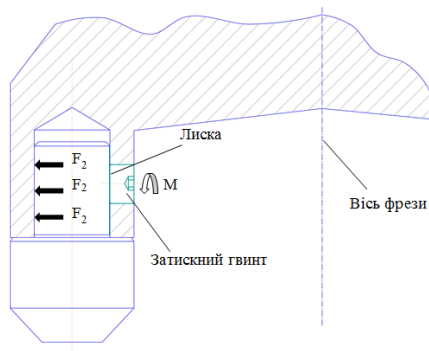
Касета з лискою на хвостовику. Закріплення у корпусі [2]
